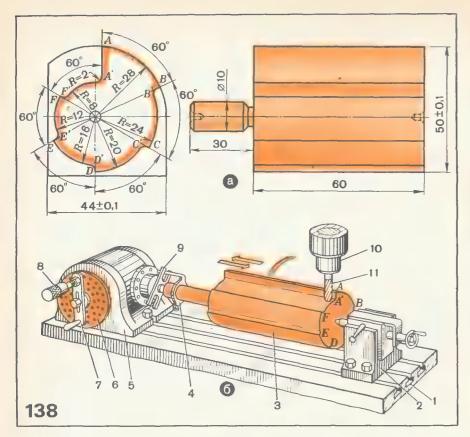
Обработка цилиндрической поверхности пуансона и делительном нриспособлении:
